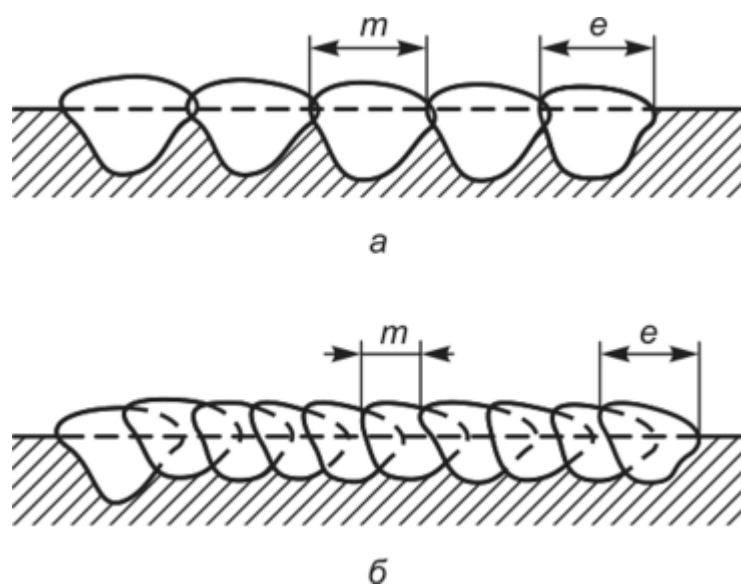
Схема наплавки валиков при разной величине шага наплавки:
